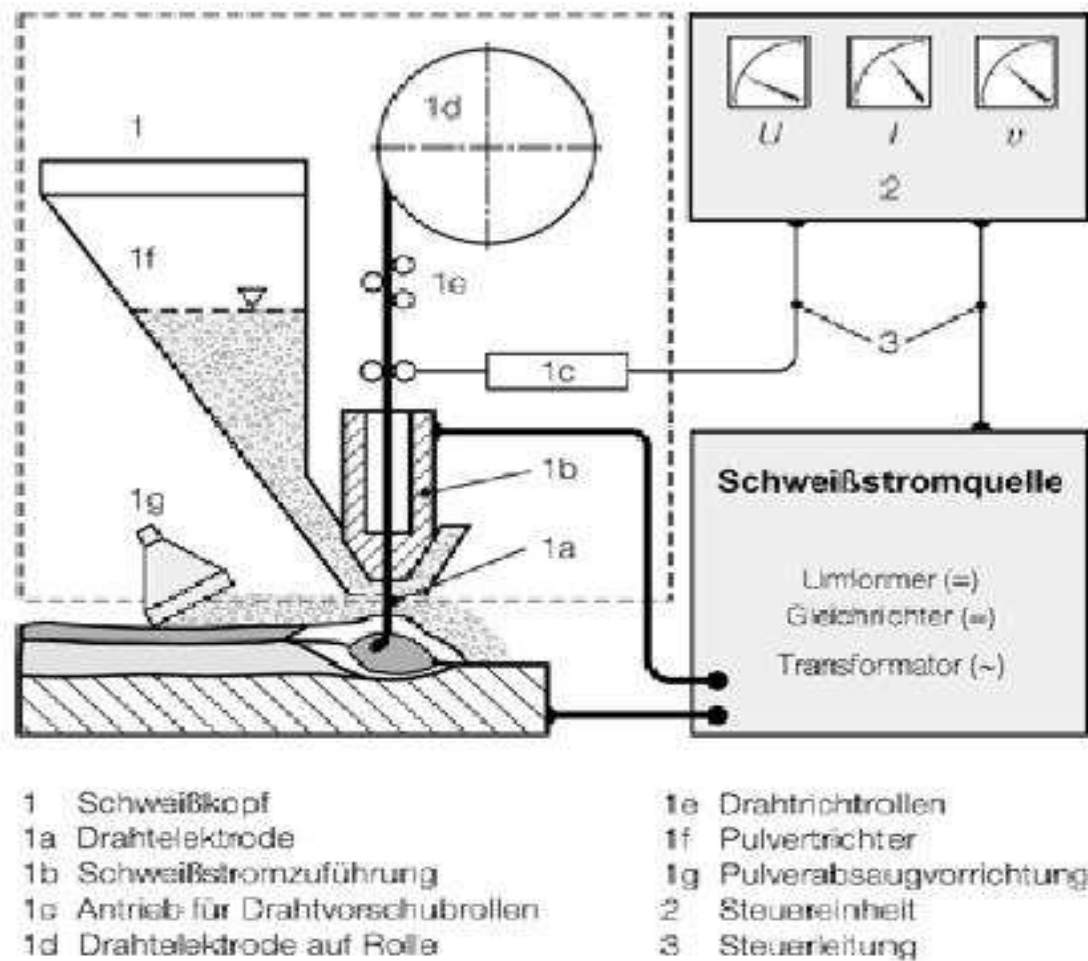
Aufbau einer UP-Schweißanlage<sup>[ST03]</sup>
